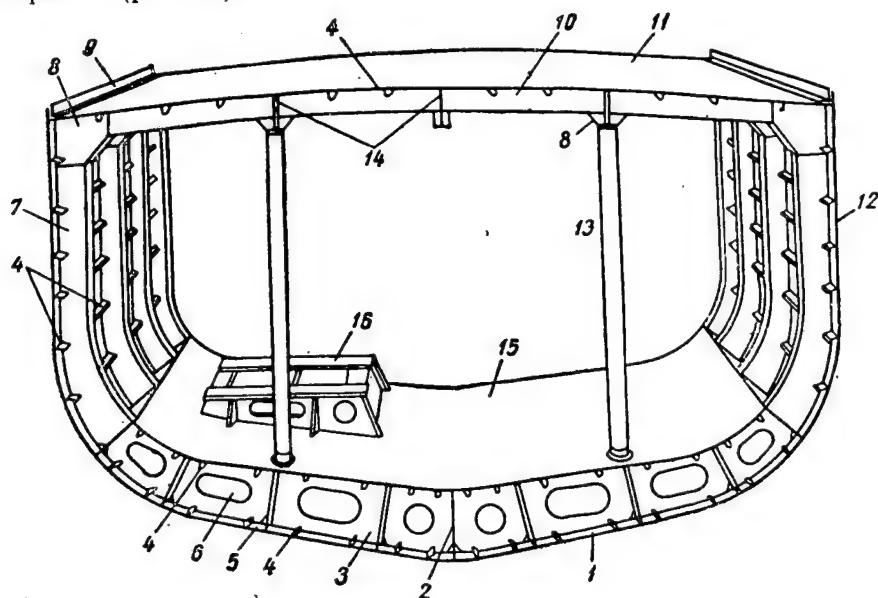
Поперечный разрез судна сварной конструкции:
